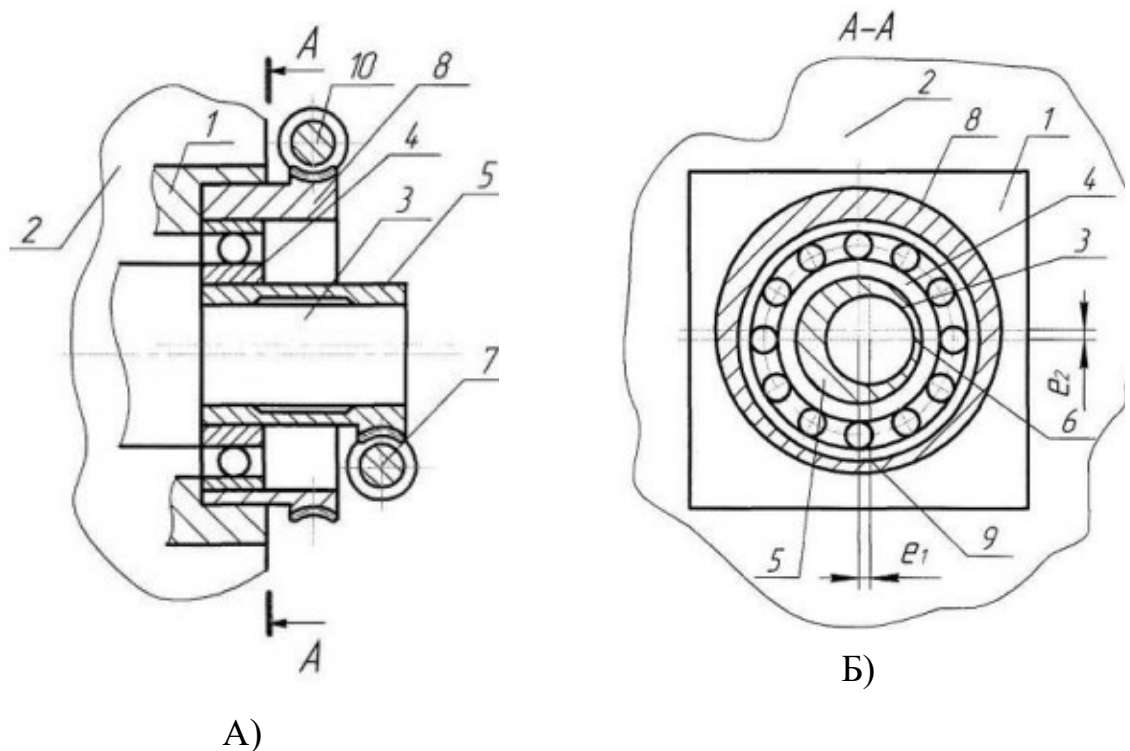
Механізм повороту: А) механізм регулювання величини перехрещення валків; Б) переріз А – А
